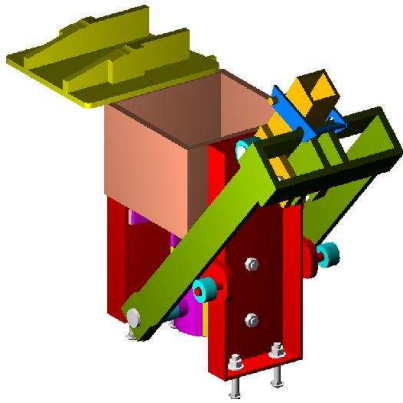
Irpha-Ram-Contrafuerte armado-Sistema Constructivo (créditos: Albarracín- Dubos 2010)
